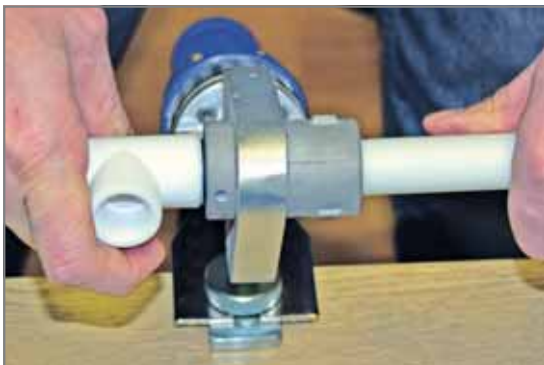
Сварка вразруб полипропиленовой трубы
